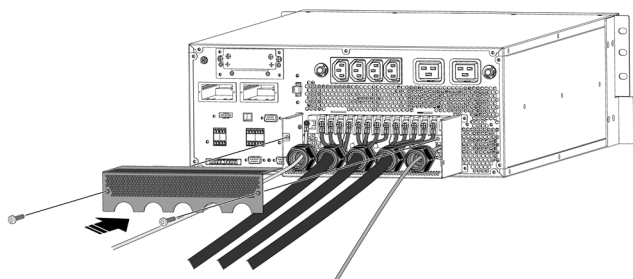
Re-ubicación de la cubierta de protección de los terminales de conexión versión rack.
